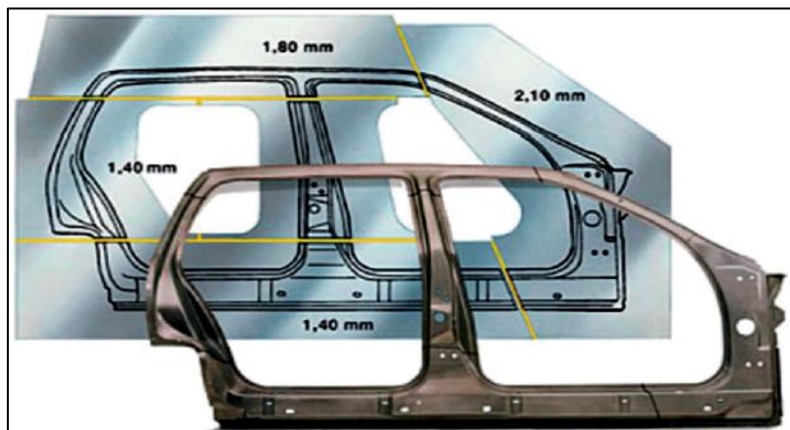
Exemplo de painel lateral soldado a laser e estampado, com diferentes dimensões num mesmo blank
